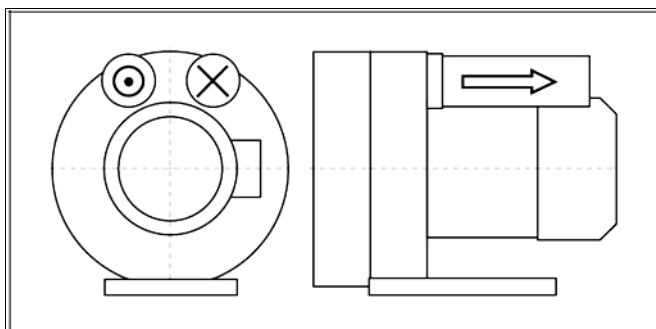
Двухпоточная конструкция вакуумного насоса/компрессора с двумя рабочими колесами.
